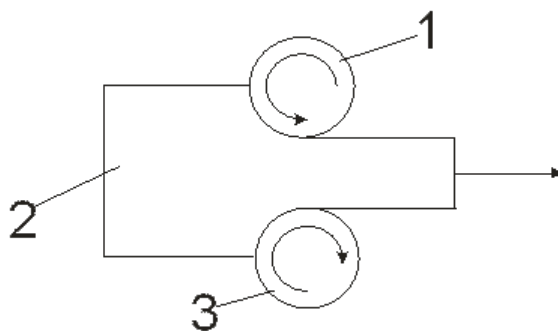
Продольная прокатка: 1 – верхний валок; 2 – нижний валок; 3 – заготовка
